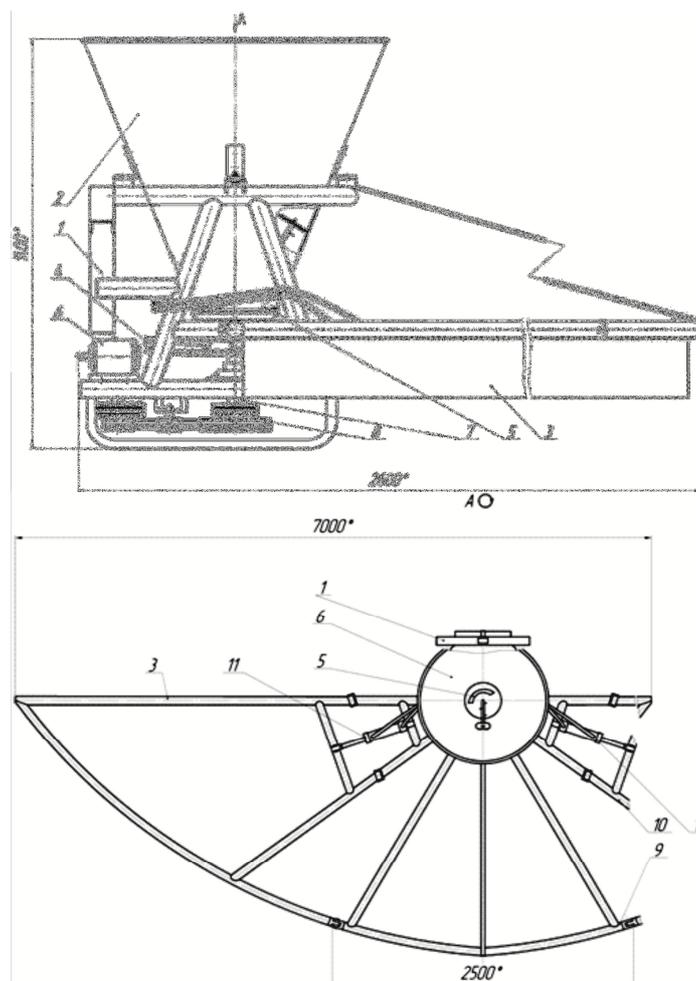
Общий вид навесного разбрасывателя песка и реагентов:
